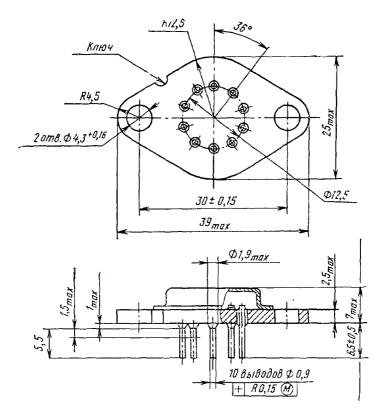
Конструкция металлостеклянного корпуса 3204 (311.10-1)
